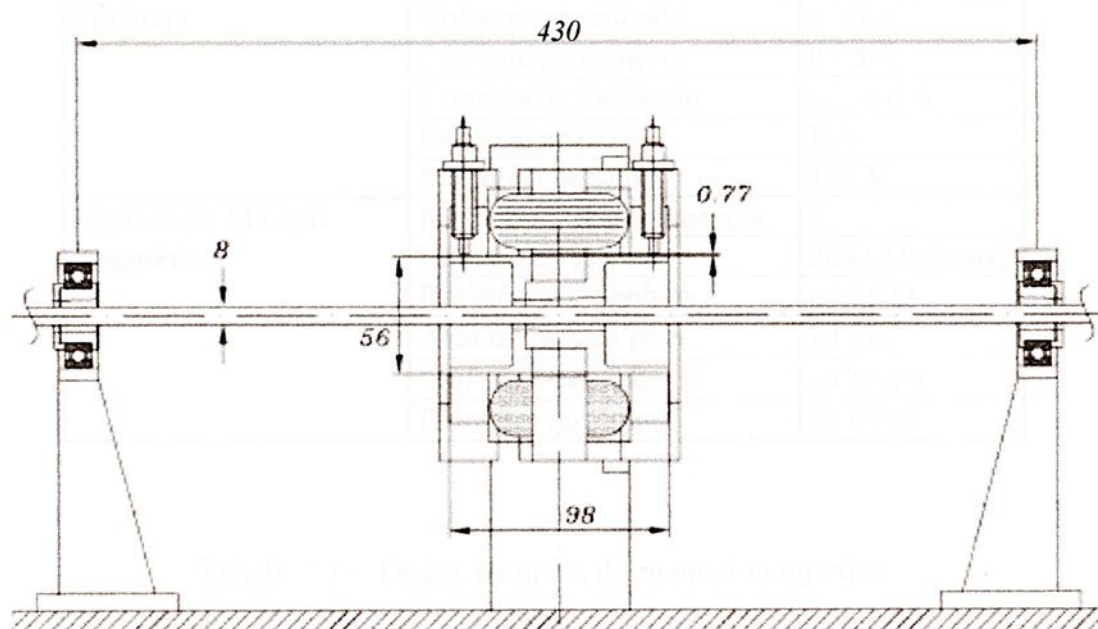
Dimensões básicas de construção do rotor Jeffcott com mancal magnético.
